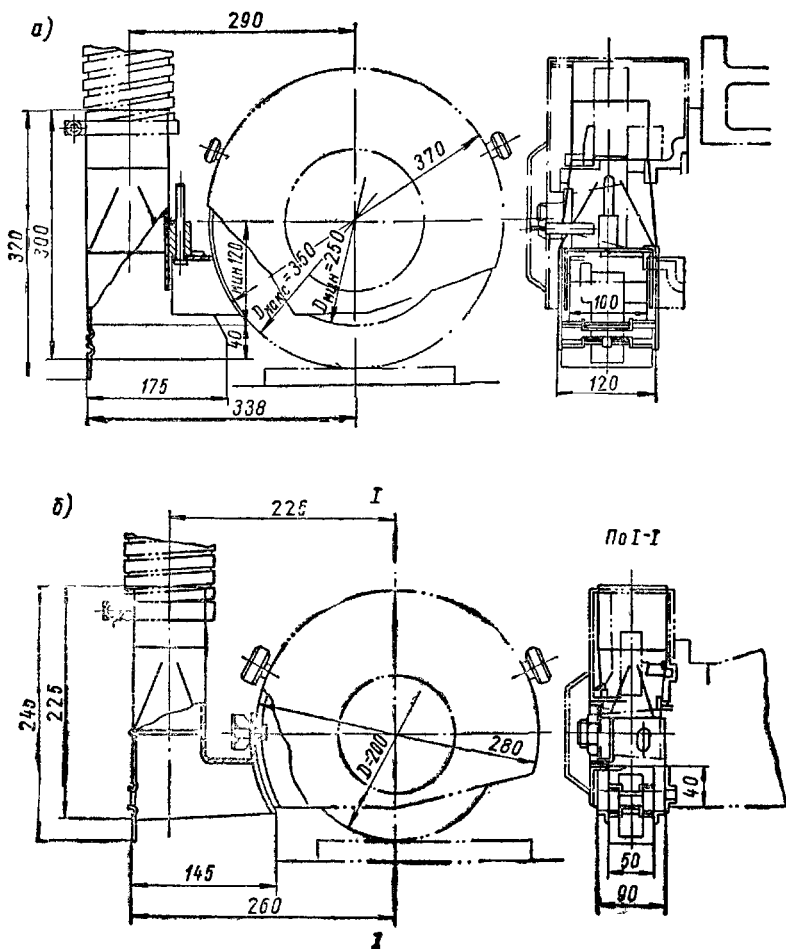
Защитно-обеспыливающий кожух к плоскошлифовальным станкам
